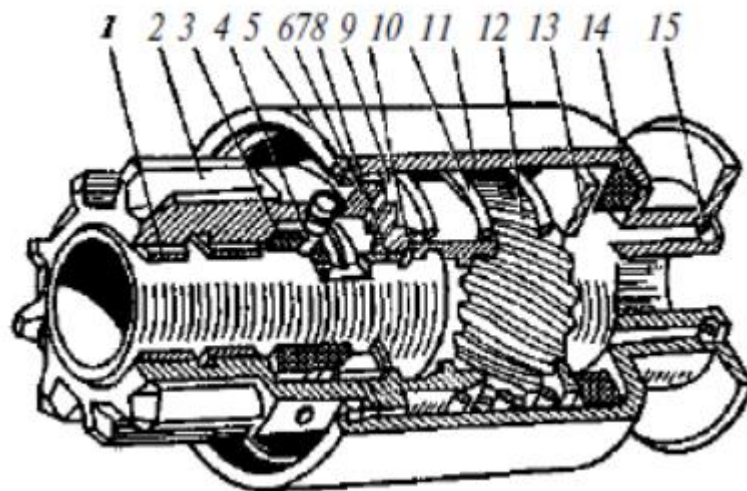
Храповая муфта свободного хода: 1 – подшипник; 2 – шестерня; 3 – сухарь; 4 – направляющий штифт; 5 и 15 – замковые кольца; 6 – ведомая половина храповой муфты; 7 – коническая направляющая втулка; 8 – ведущая половина храповой муфты; 9 и 13 – шайбы; 10 – пружина; 11 – корпус; 12 – шлицевая направляющая втулка; 14 – буферное резиновое кольцо
